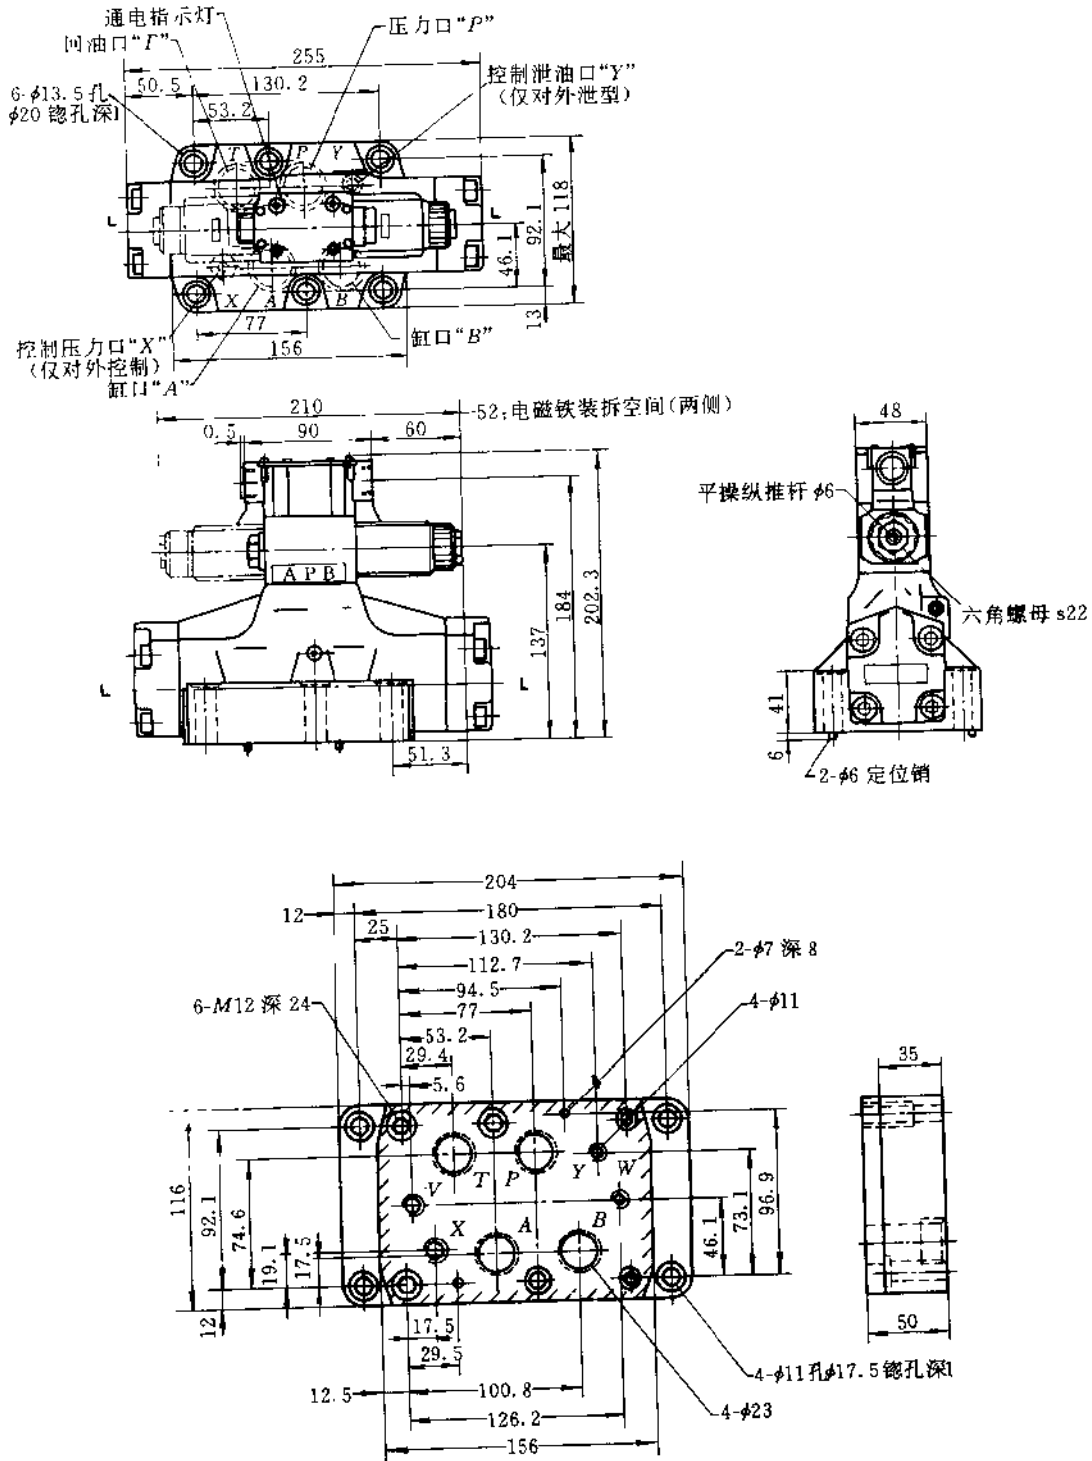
DSHG 06 型电液换向阀外形及连接尺寸图
